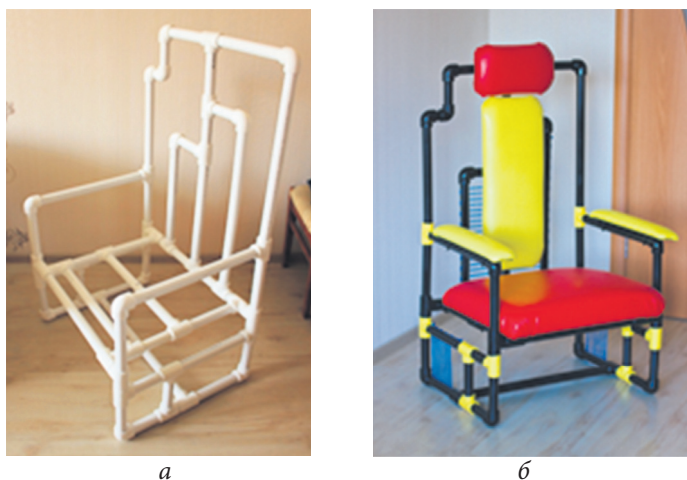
Изготовление опытного образца изделия из труб ПВХ: а — каркас кресла из труб ПВХ; б — опытный образец кресла
